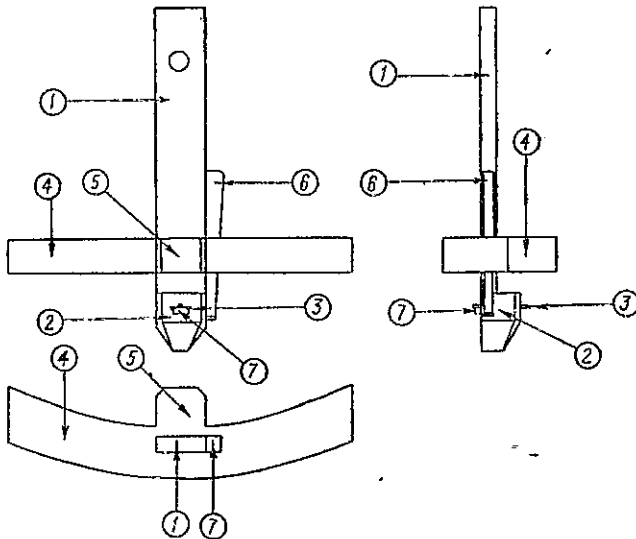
«Гребень»: 1—планка с головкой, 2—головка, 3—резцы, 4—колодка, 5—опорный выступ, 6—клинья для закрепления планки, 7—клинья для закрепления железки
